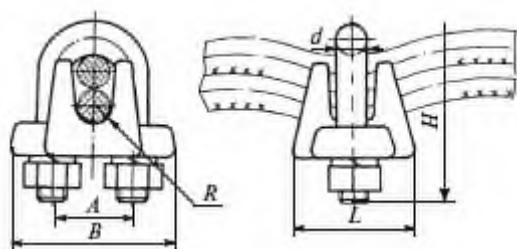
Клыковой зажим типа КС для крепления стальных канатов
